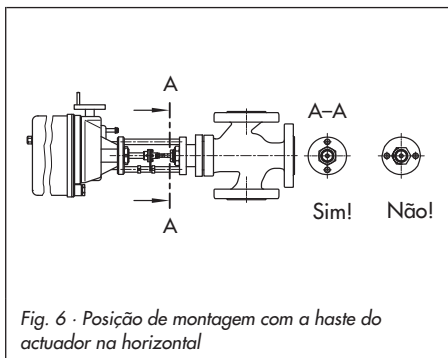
· Posição de montagem com a haste do actuador na horizontal
